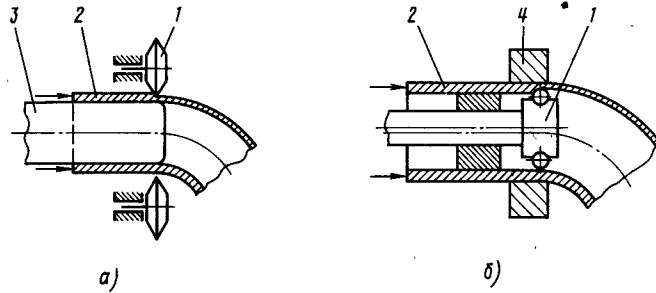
Схема гибки труб эксцентричным ротационным выдавливанием (раскаткой): а — наружным; б — внутренним; 1 — раскатный инструмент; 2 — изгибаемая труба; 3 — оправка; 4 — кольцо
